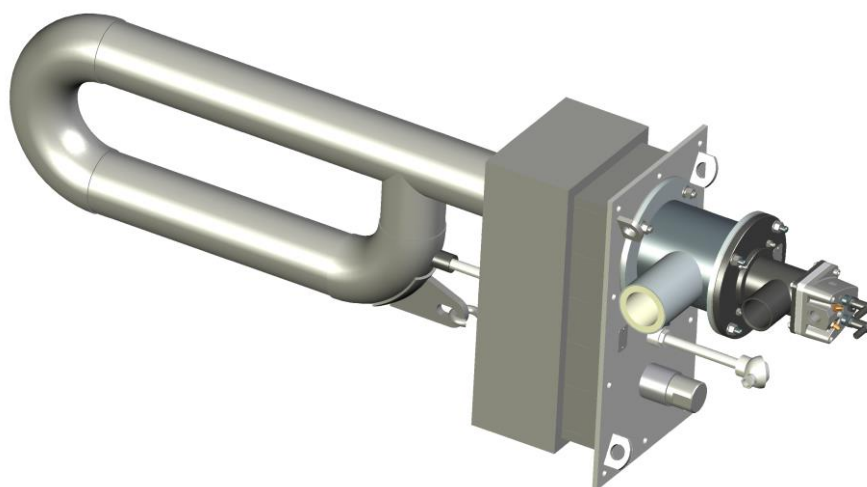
Внешний вид горелки газовой РЕ-ТЕРМ 80/65НВ-0/535-(34А)ТР
